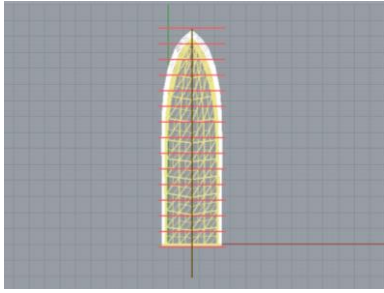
Vista de las cuadernas en planta por Rhinoceros
